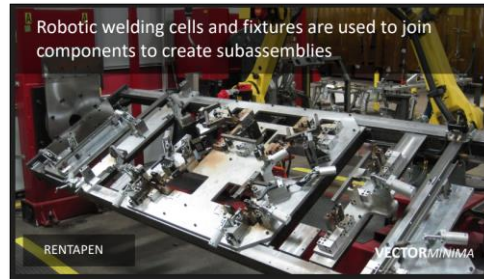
Máquina CNC robotizada para soldar elementos de acero.
